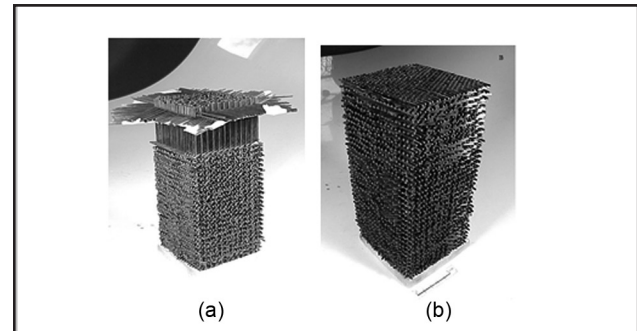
Detalle del posicionamiento de las varillas en el plan de la preforma 4d-planar.
